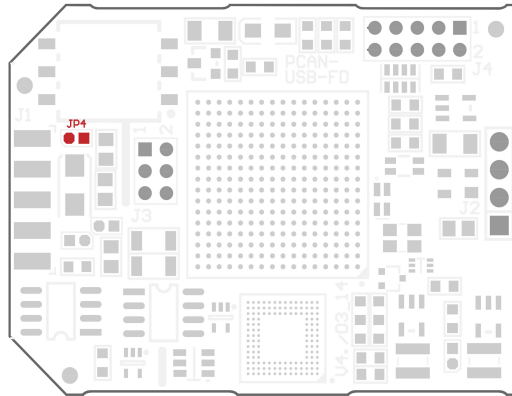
Draufsicht Platine PCAN-USB FD, Lötfeld JP4
